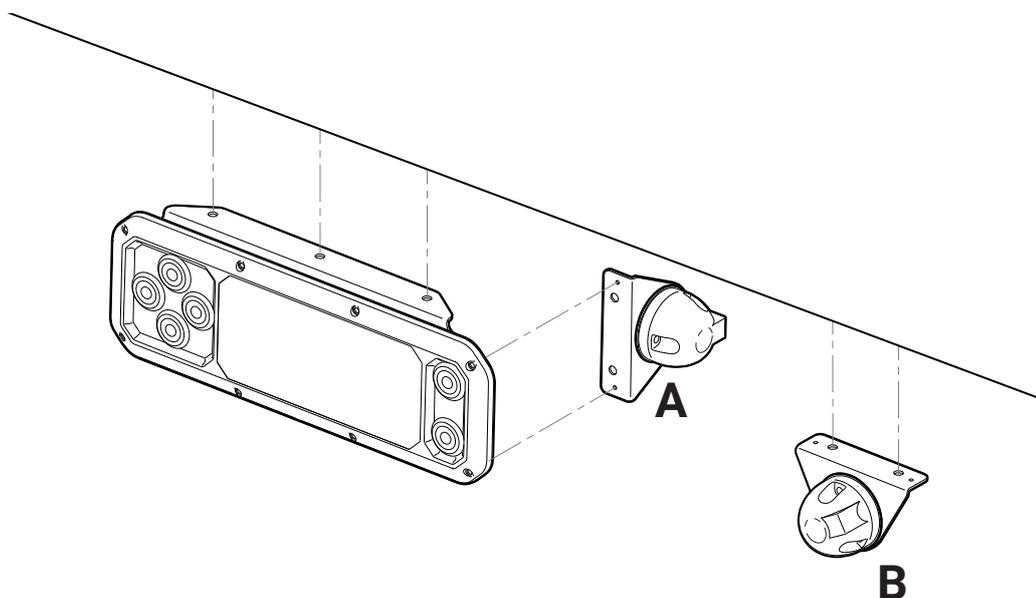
Montaje del actuador CD19 y del conector para actuador portátil
